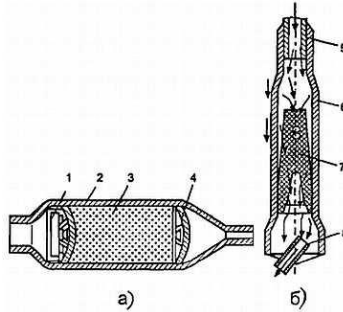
Конструкция фильтра — осушительного патрона: а — без металлокерамики: 1 — обойма сетки фильтра; 2 — корпус; 3 — адсорбент; 4 — сетка фильтра; б — с металлокерамикой: 5 — трубка конденсатора; 6 — корпус; 7 — фильтр; 8 — капиллярная трубка
